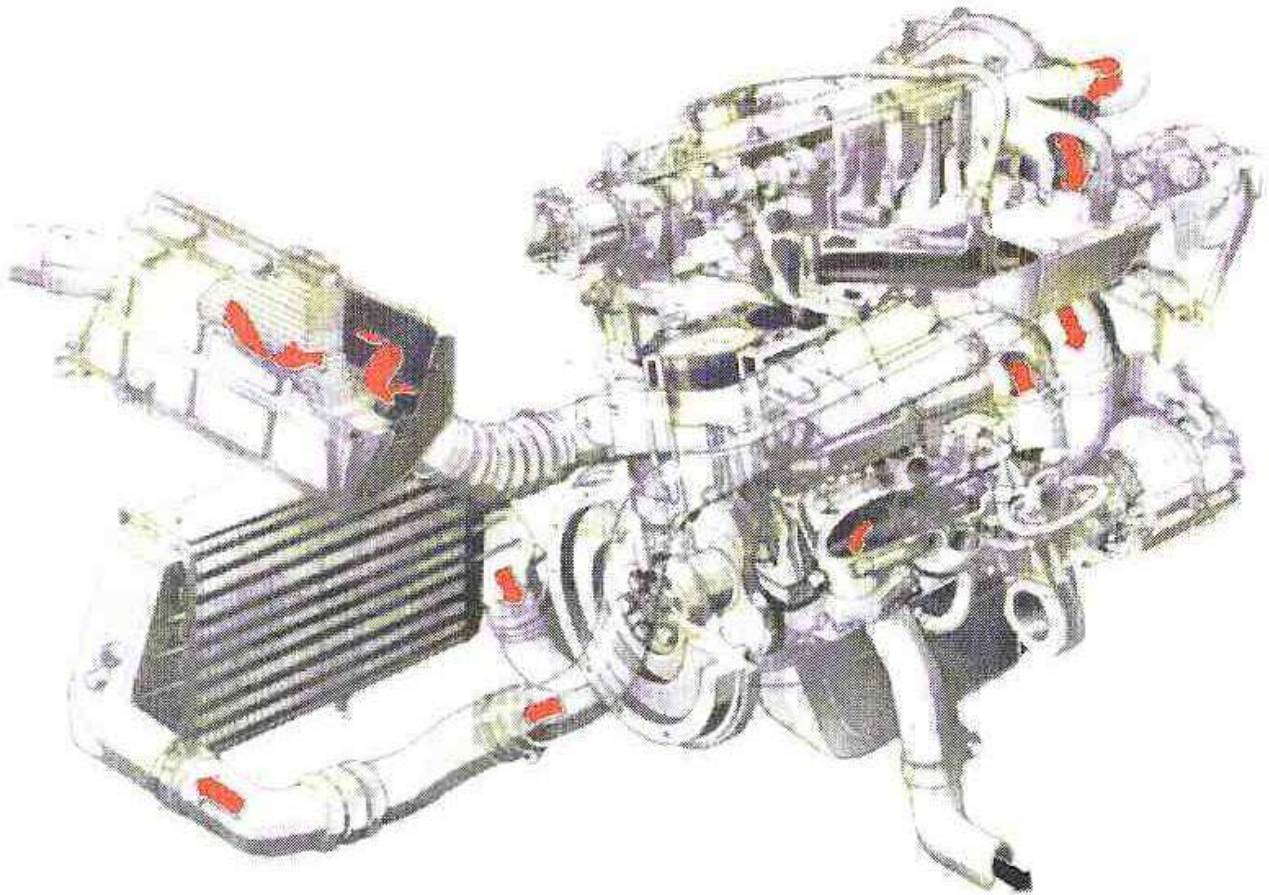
Motor de 4 cilindros turbodiesel intercooler (Fiat)
